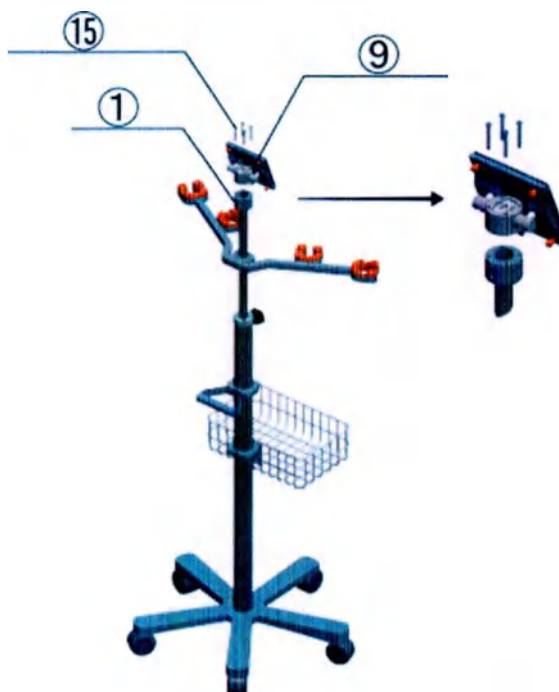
Сборка медицинской стойки Endostand Шаг 6
